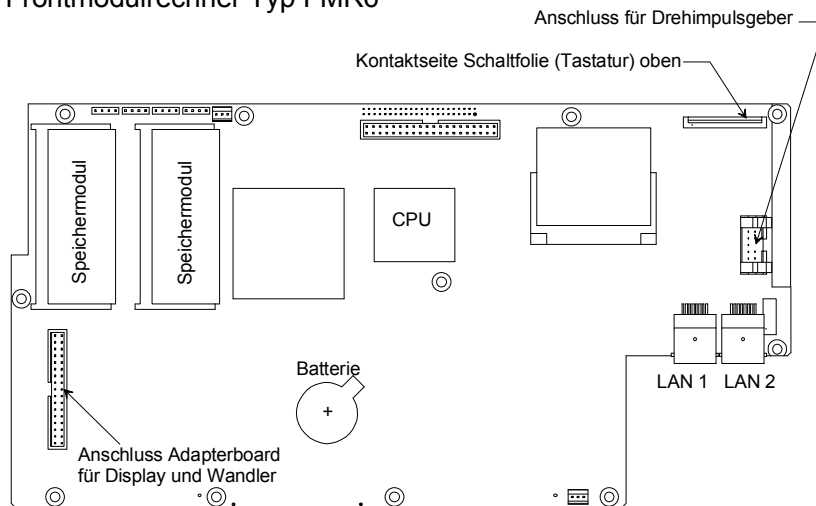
Lage der Steckkontakte auf dem Frontmodulrechner
